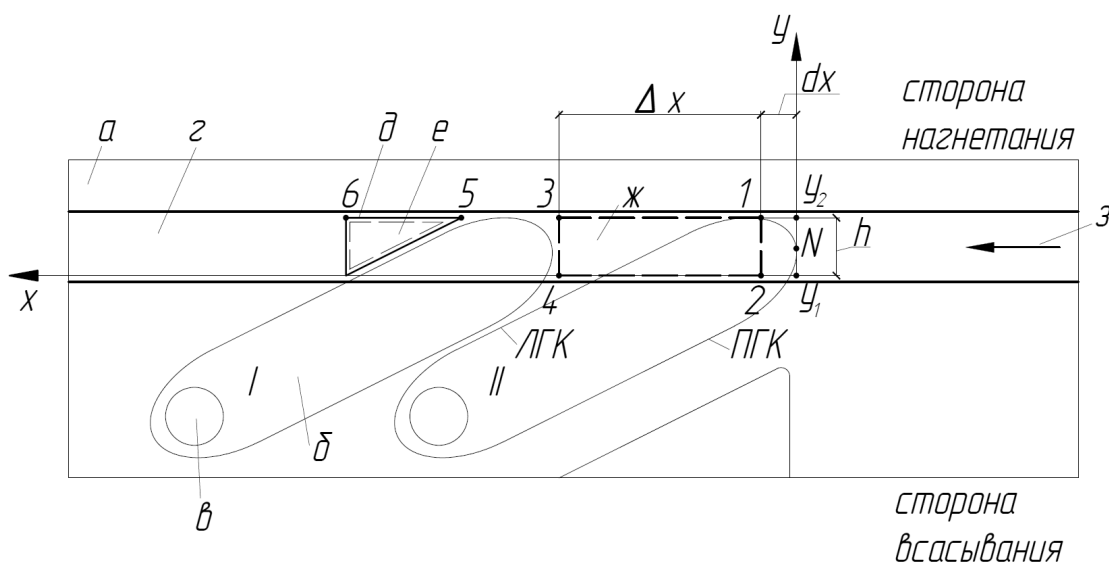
Развертка винта-ротора (2 канавки), поворотного регулировочного кольца и части корпуса в плоской системе координат
